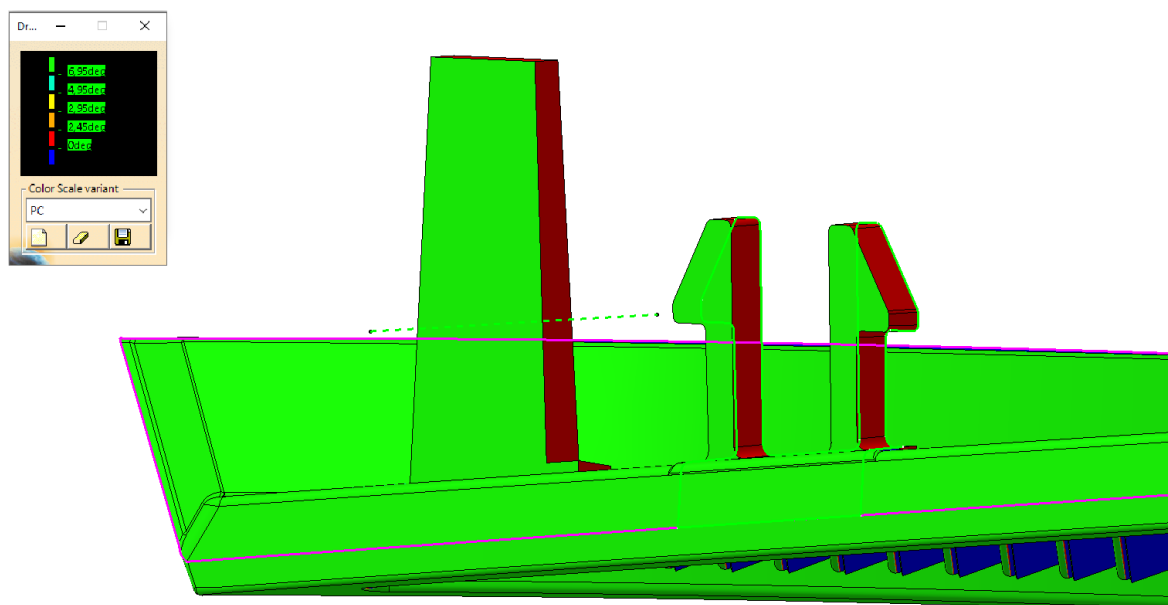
Odformování krycího rámečku A – koncept konstrukčního řešení 2.
